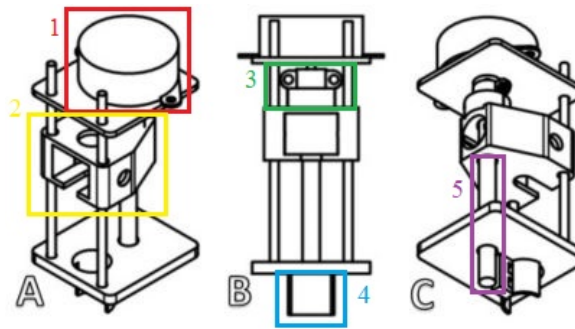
Diferentes vistas do primeiro protótipo: A – Vista frontal em 3 dimensões; B – Vista frontal em 2 dimensões; C – Vista lateral em 3 dimensões. 1- Motor de passo unipolar; 2 – Peça de acoplamento ao eletrodo; 3 – Peça de fixação do eixo do motor ao parafuso; 4 – Suporte de fixação do eletrodo; 5 – Parafuso rotativo. Do autor
